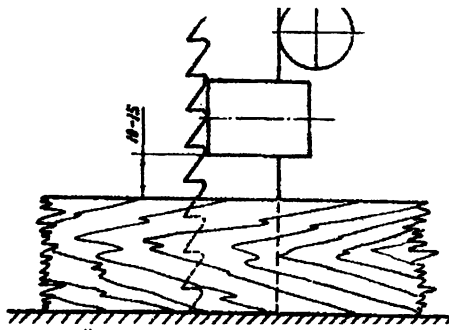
Схема настройки положения верхнего направляющего устройства
